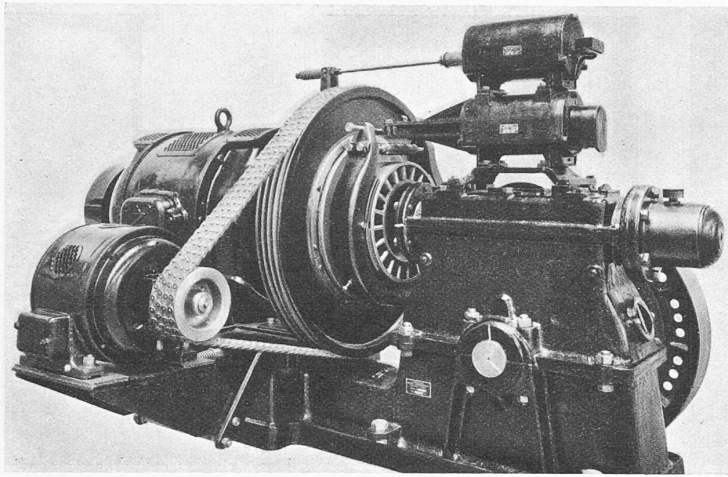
Aufzugmaschine mit Haupt- und Feineinstellmotor am rechten Ufer.
